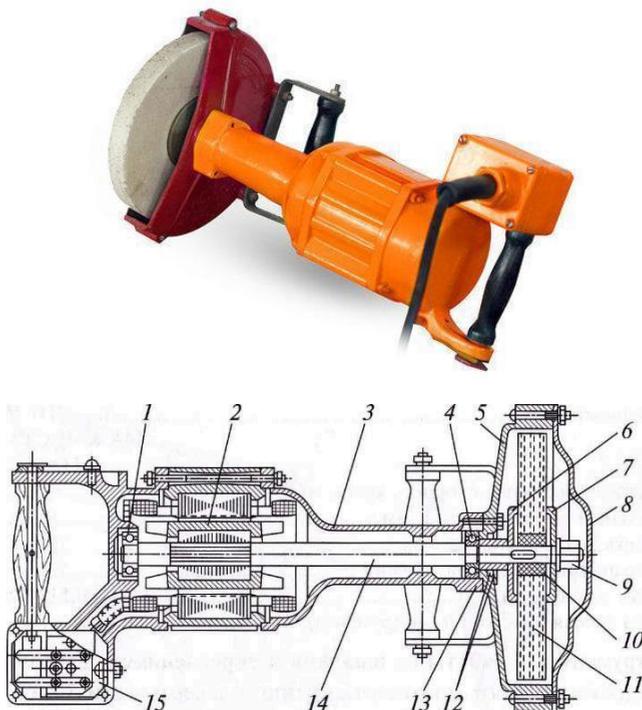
Рельсошлифовалка МРШ-3
